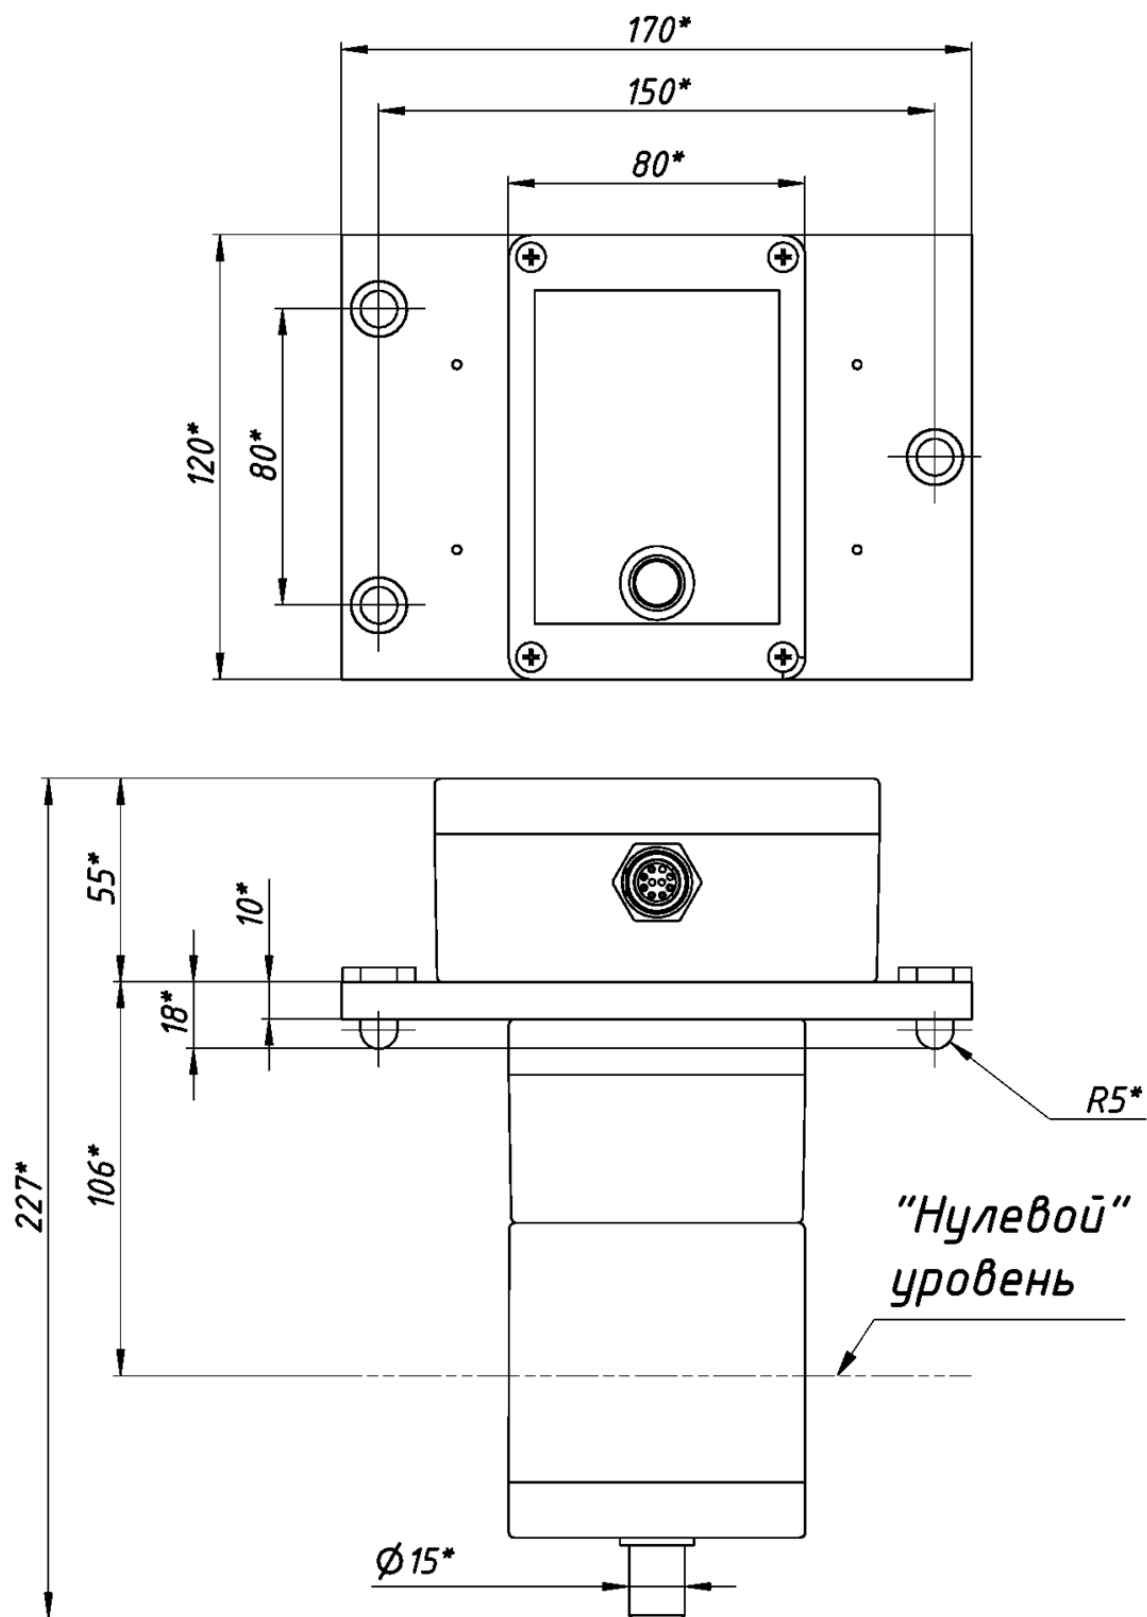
Габаритные и установочные размеры измерителя в исполнении №03.
